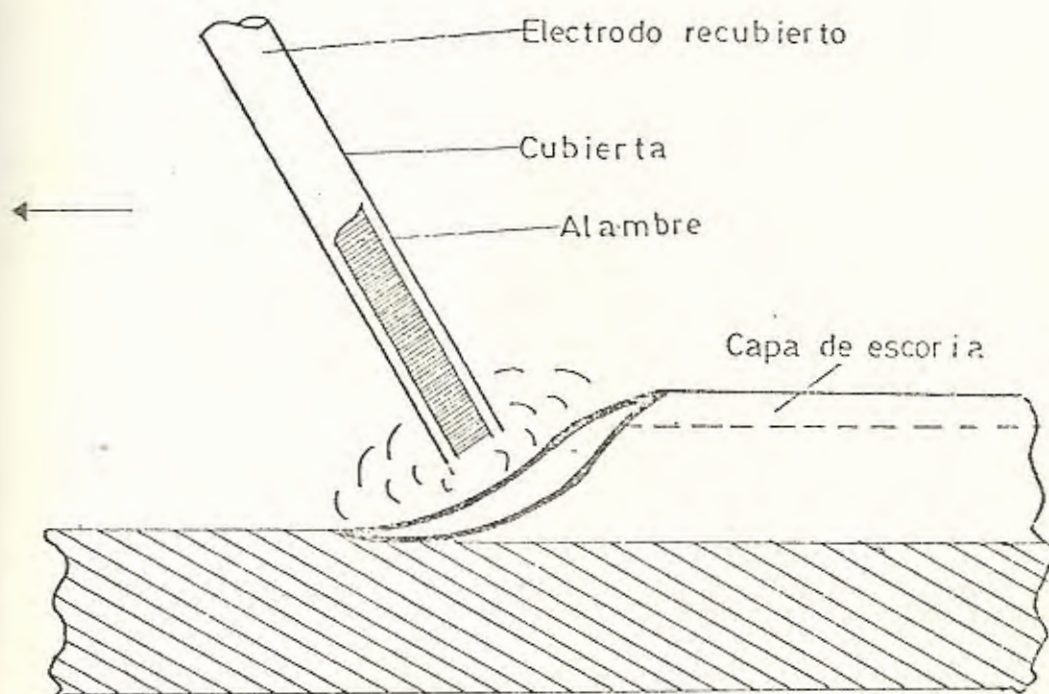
SOLDADURA POR ARCO CON ELECTRODO REVESTIDO
